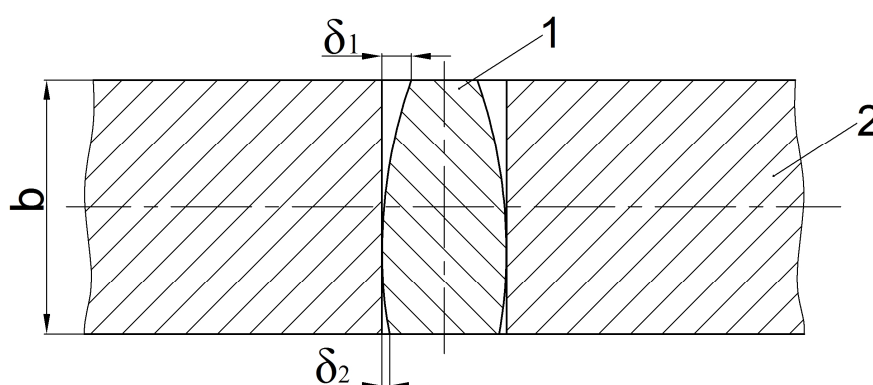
Схема зацепления зубьев шестерни и колеса в продольном сечении
